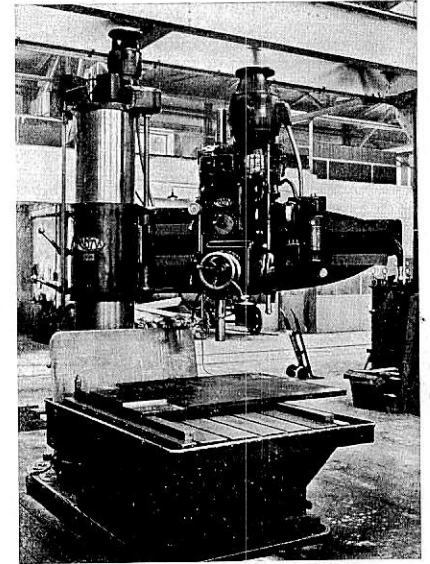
Radialbohrmaschine mit Spindelstockmotor, besonderem Hubmotor und Druckknopfschaltung.
